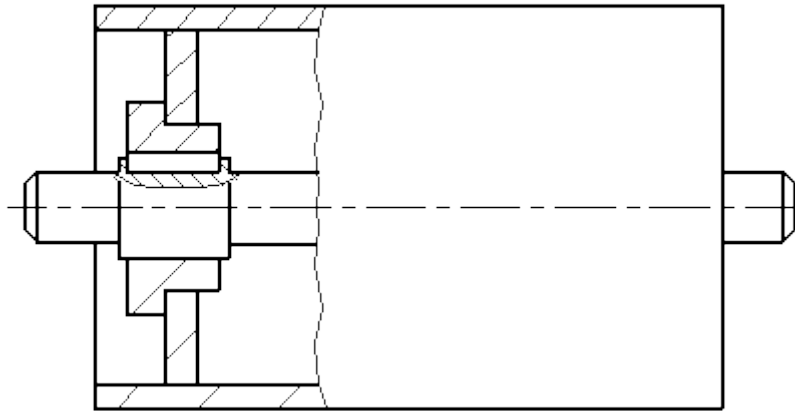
Пример изображения сварной сборочной единицы на сборочном чертеже изделия
